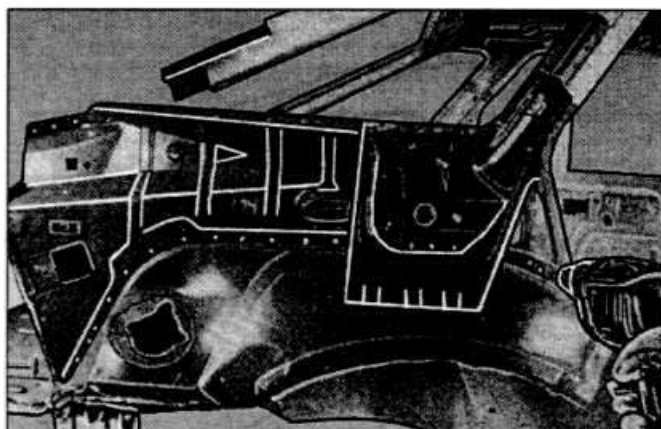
Высверливание точек сварки заднего надколесного кожуха
